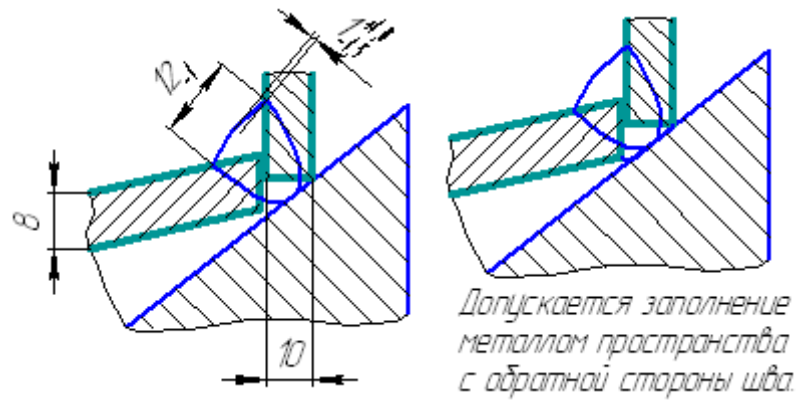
Эскиз сварного шва. Геометрические параметры
